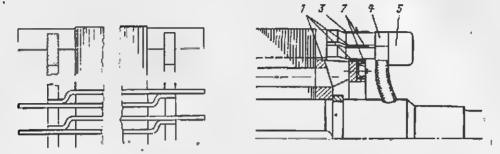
Принципнальная конструкция сварной алюминисвой клетки ротора двигателей с h>355 мм.
